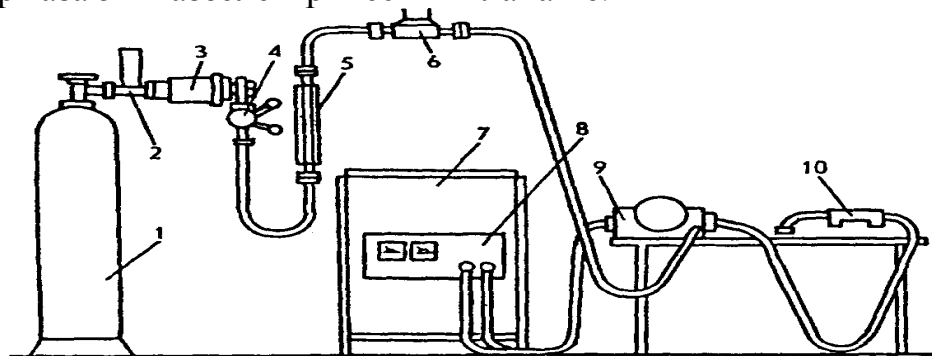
Рабочее место для сварки в среде углекислого газа:
